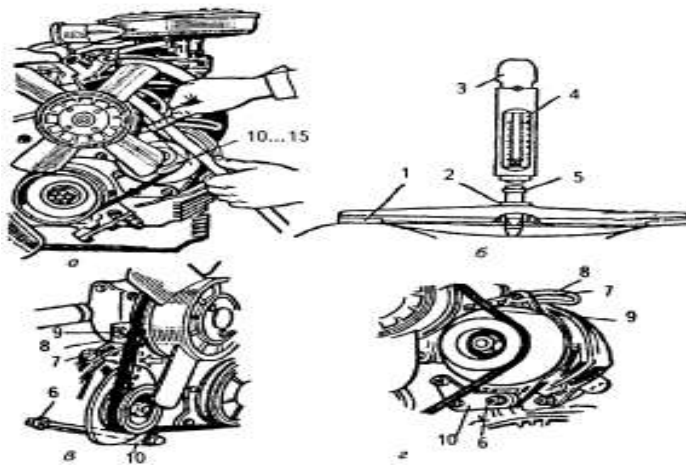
Проверка и натяжение ремня привода жидкостного насоса и генератора: а — проверка натяжения ремня с помощью линейки с рейкой на двигателе УЗАМ-412; б — проверка натяжения ремня с помощью динамометрического устройства; в — натяжение ремня на двигателях ВАЗ-2105 и -2106; г — натяжение ремня на двигателях УЗАМ-331 и 412; 1 — планка; 2 — упорная втулка; 3 — ручка; 4 — шкала; 5 — буртик штока; 6 — болты и гайки крепления генератора к болту цилиндров двигателя; 7 — гайка крепления генератора к планке; 8 — натяжная планка; 9 — гайка крепления натяжной планки к блоку цилиндров; 10 — кронштейн крепления генератора к блоку цилиндров
